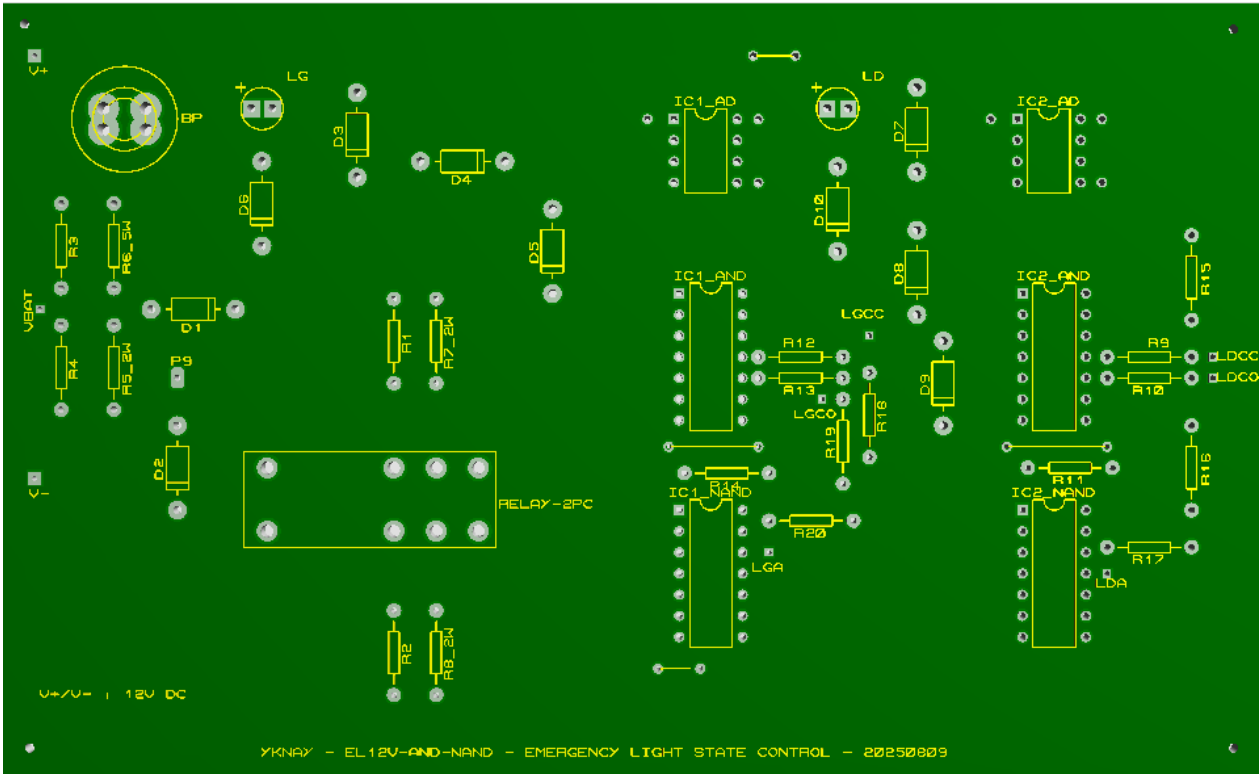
PCB - Circuit électronique, vue arrière des composants et points de connexions
